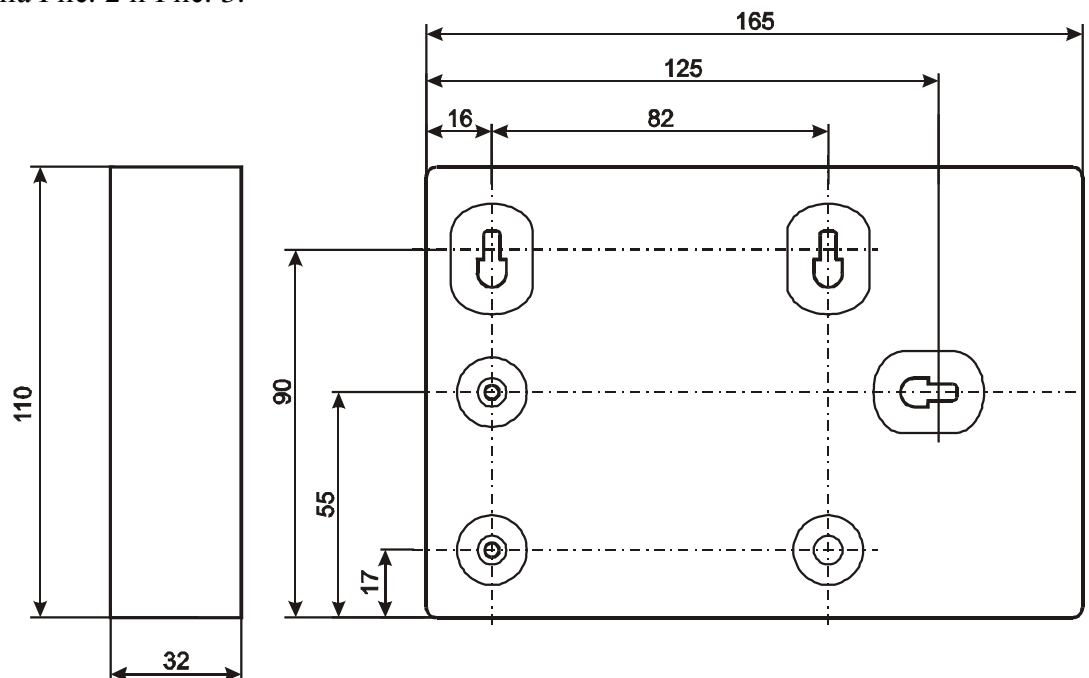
Внешний вид и габаритные размеры БРЛ в исп. IP20
